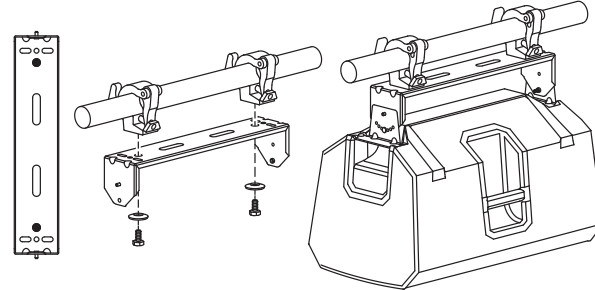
Montaje horizontal con abrazaderas para celosía TCA-1
